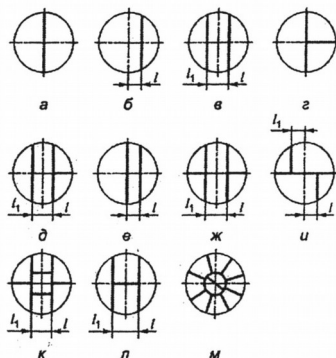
Расположение сварных швов заготовок выпуклых днищ
